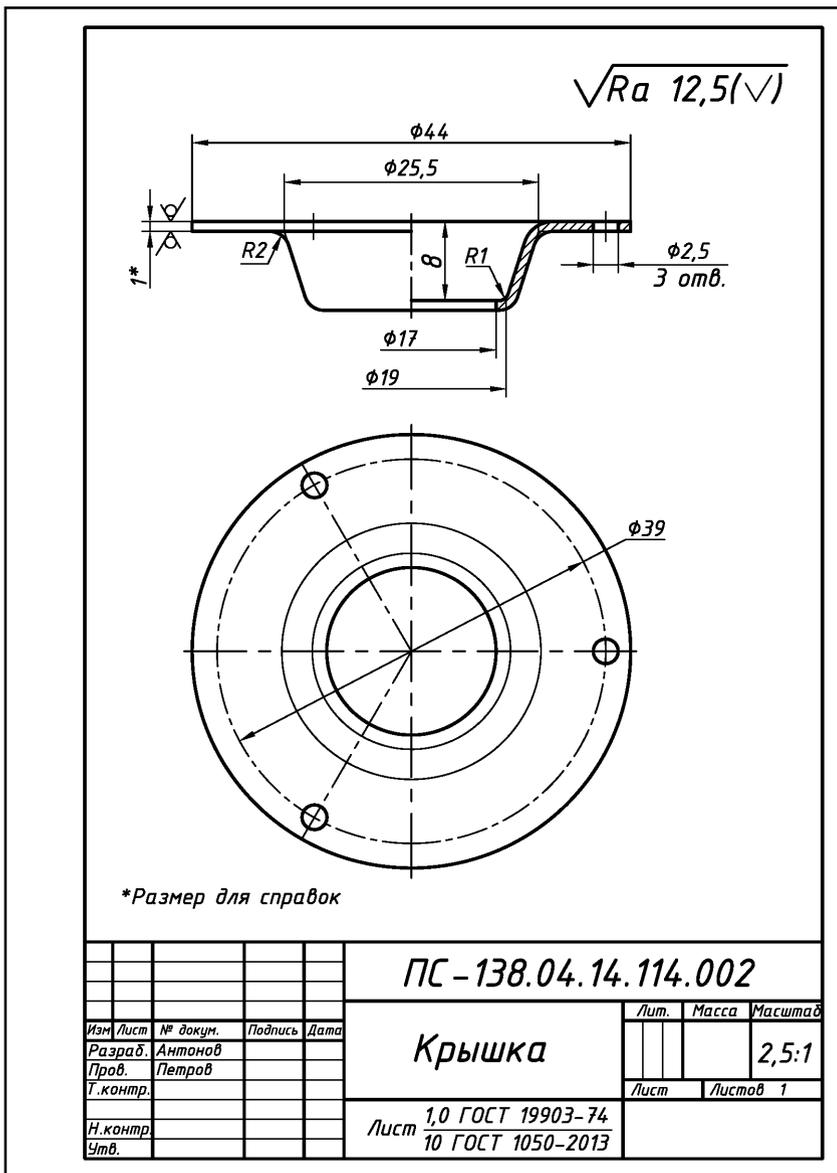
Оформление рабочего чертежа вытянутой детали из тонколистового металла
